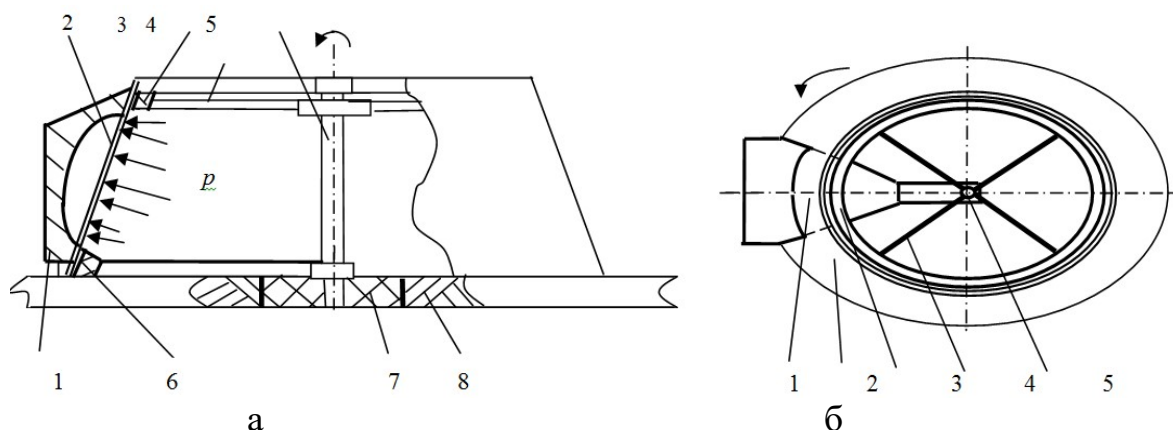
Схема стандовой штамповки с использованием термофизических методов локальной штамповки: а, б – фронтальный и горизонтальный вид: 1 – матрица-сектор; 2 – пространственный полуфабрикат; 3 – прижим; 4 – упор; 5 – ось; 6 – основание; 7 – втулка
